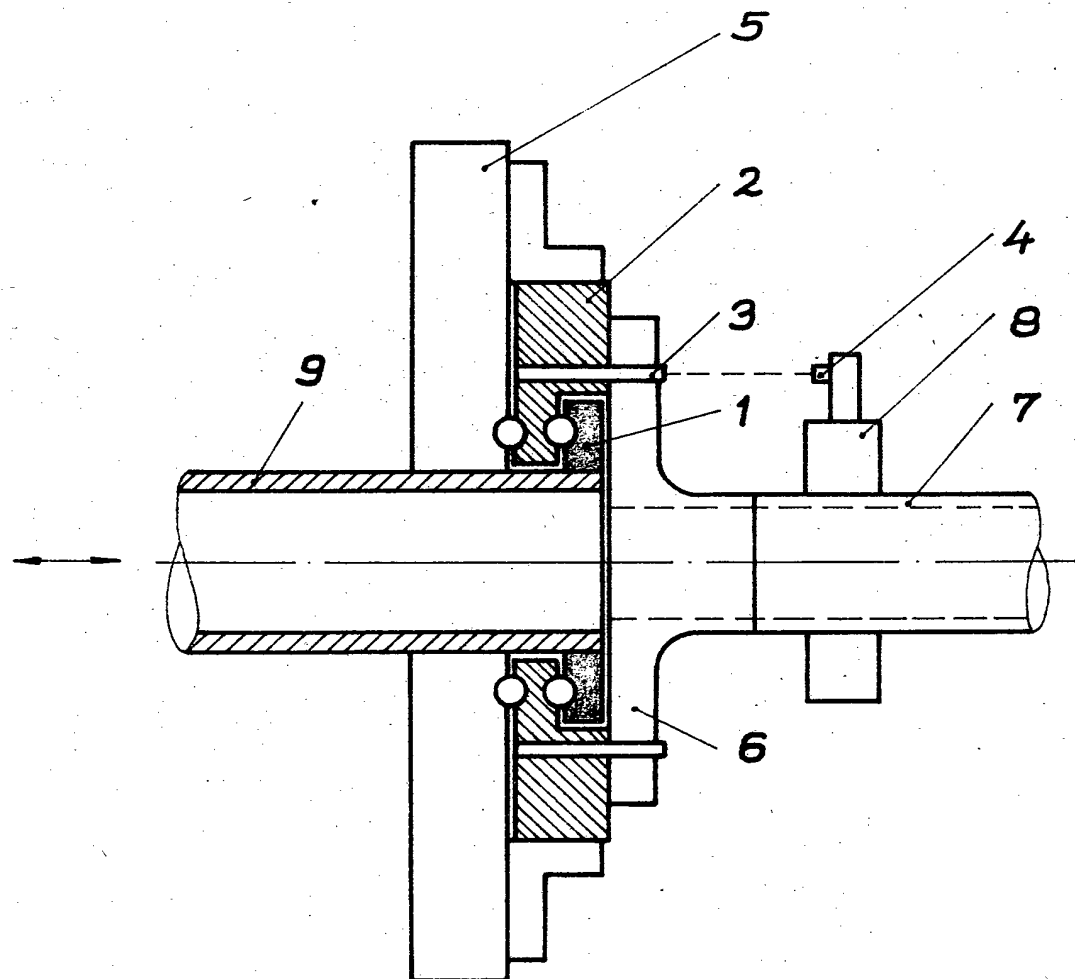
Einrichtung für Reibschweißmaschinen zur Phaseneinstellung der Schweißteile
